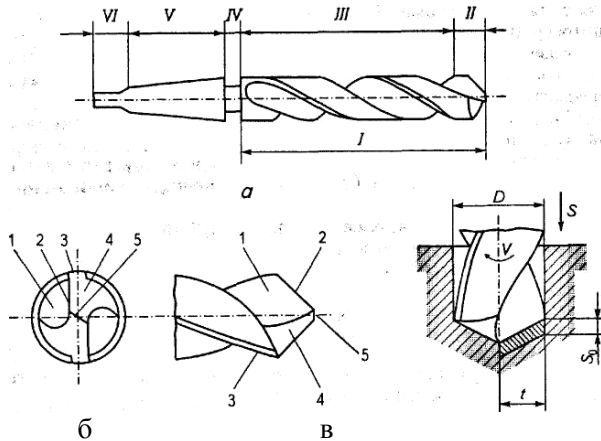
Елементи спірального свердла (а, б) і розміри зрізаного шару металу (в)
